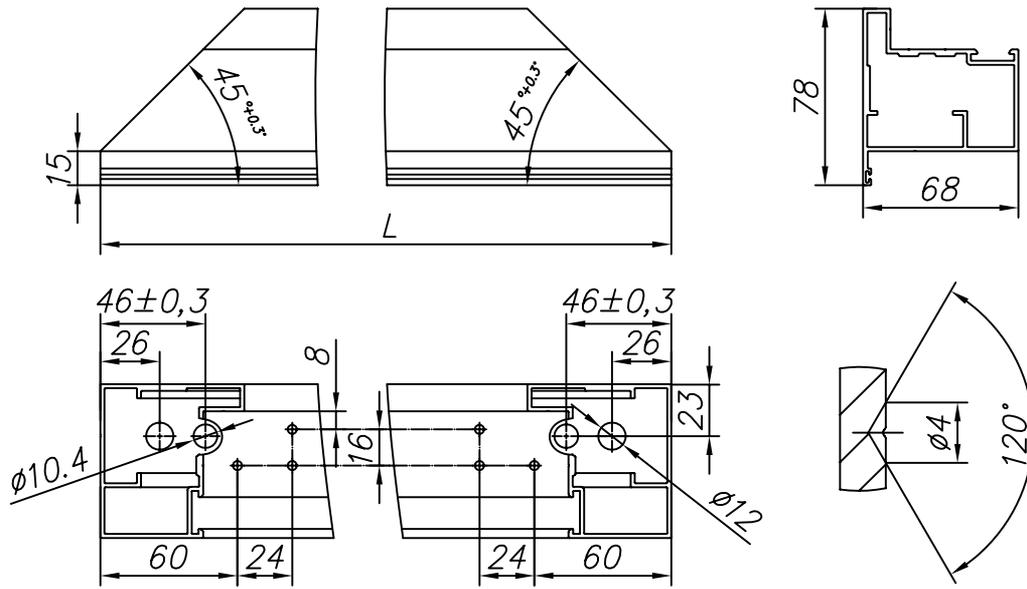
Изготовление стойки без паза для замка из профиля FLGU.400.0108 (открывание наружу)
